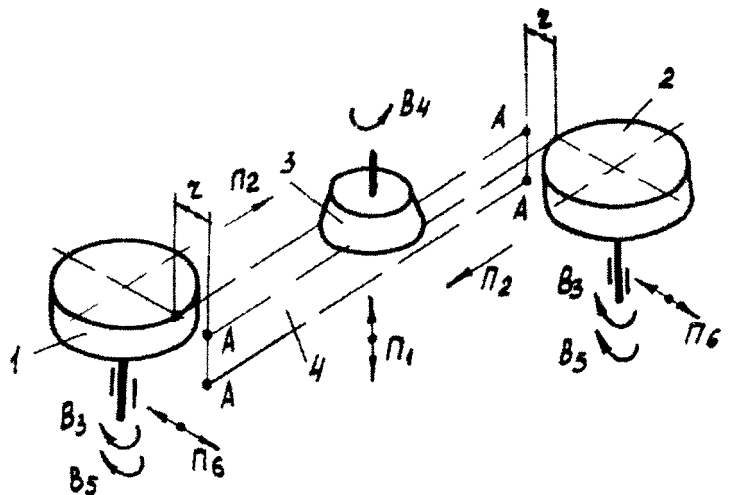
Способ долбления двух зубчатых колес при встречном движении врезания
